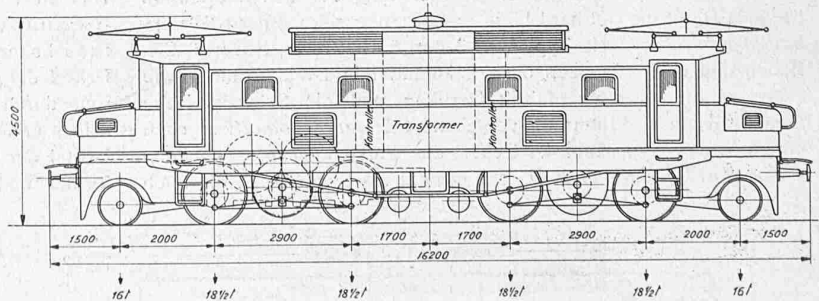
Probe-Schnellzuglokomotive der M. F. O., 2250 PS. — Typenskizze 1:150.
